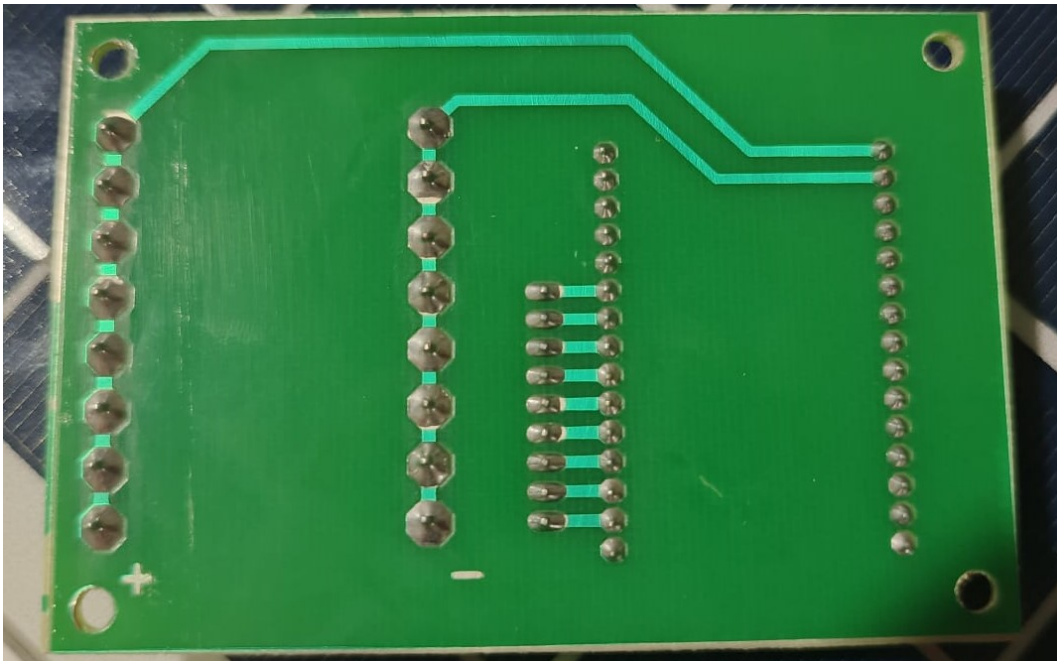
Soldado de pcb terminado. Fuente: Autores.
